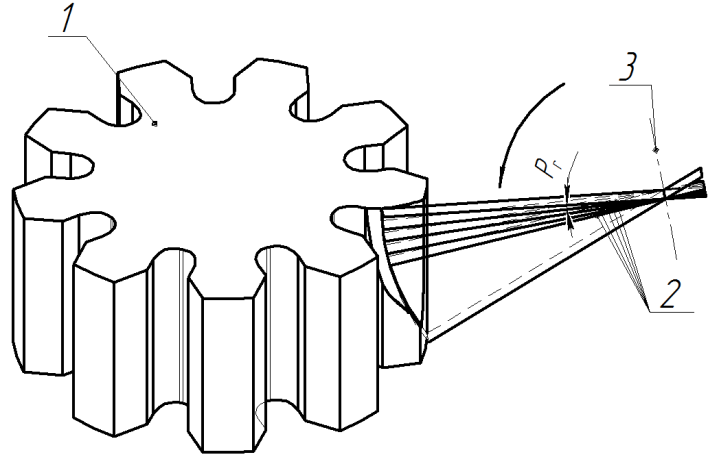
Схема розташування радіальних січних площин при черв'ячно-контурному зубофрезеруванні
